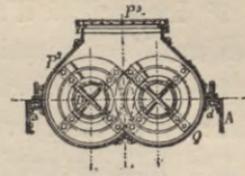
Coupe suivant XX de la figure 128 faisant voir les barrettes hélicoïdales montées sur manchons en fer creux.
